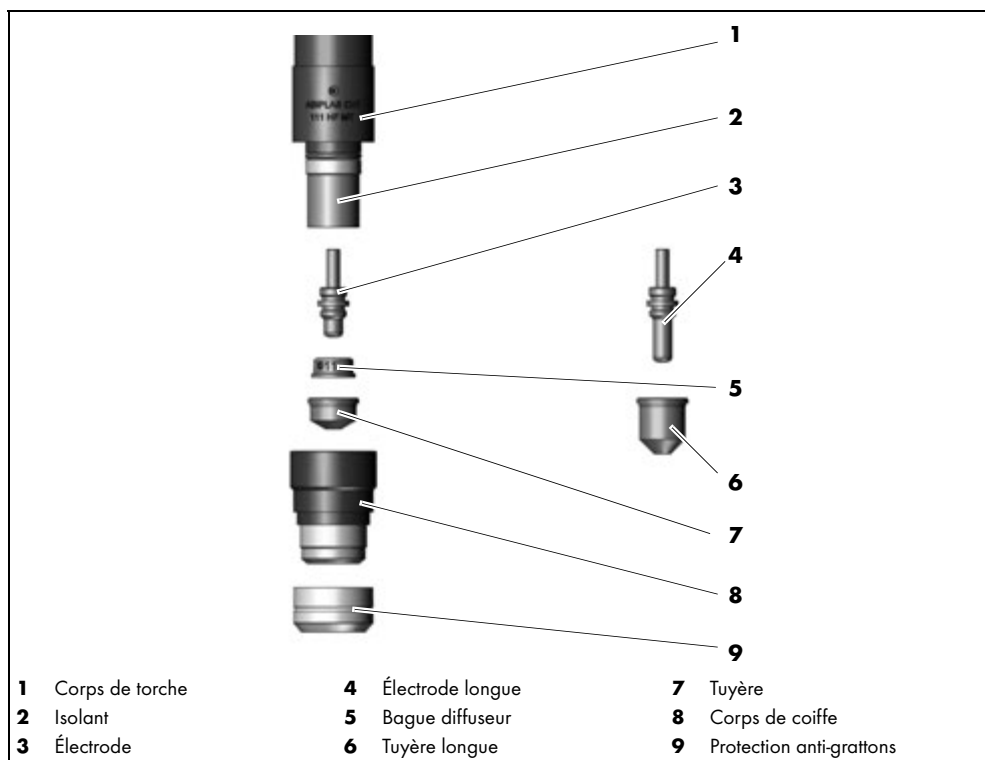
Vue d'ensemble d'ABIPLAS® CUT 71 HF MT
